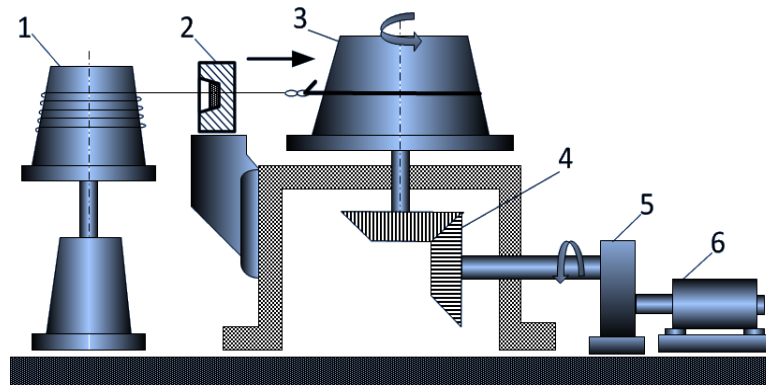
Одноразовий волочильний стан складається з вертушки для установки бухту дроту – 1; волоки – 2; обертового барабану – 3; левареджа – 4; редуктор – 5; двигун – 6
